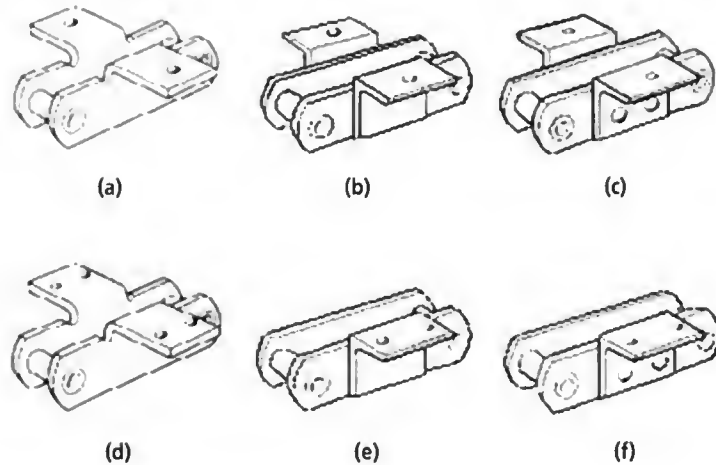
(a) Plaque attache K1 (b) soudée ou (c) rivée et (d) plaque attache K2 (e) soudée ou (f) rivée.
